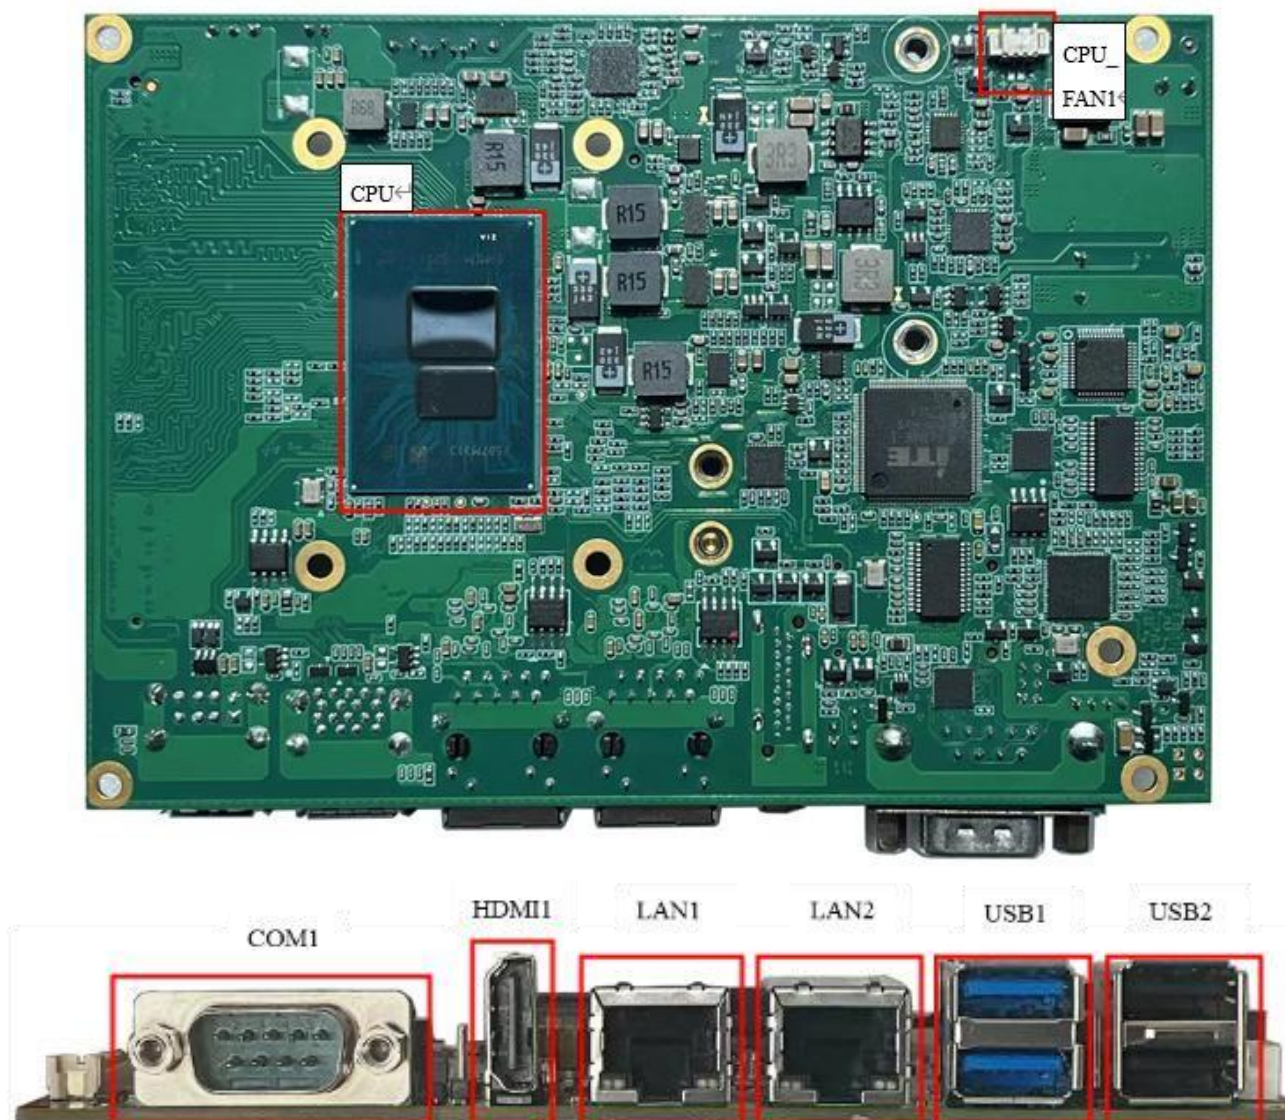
Position der Jumper und Anschlüsse – Unterseite des Mainboards
